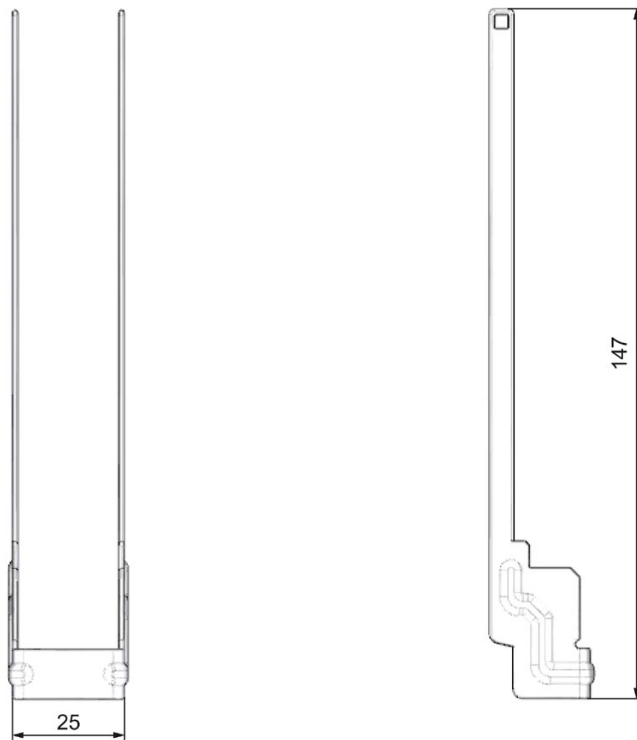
Maßbild Schirmbügel für 35 mm-Module
